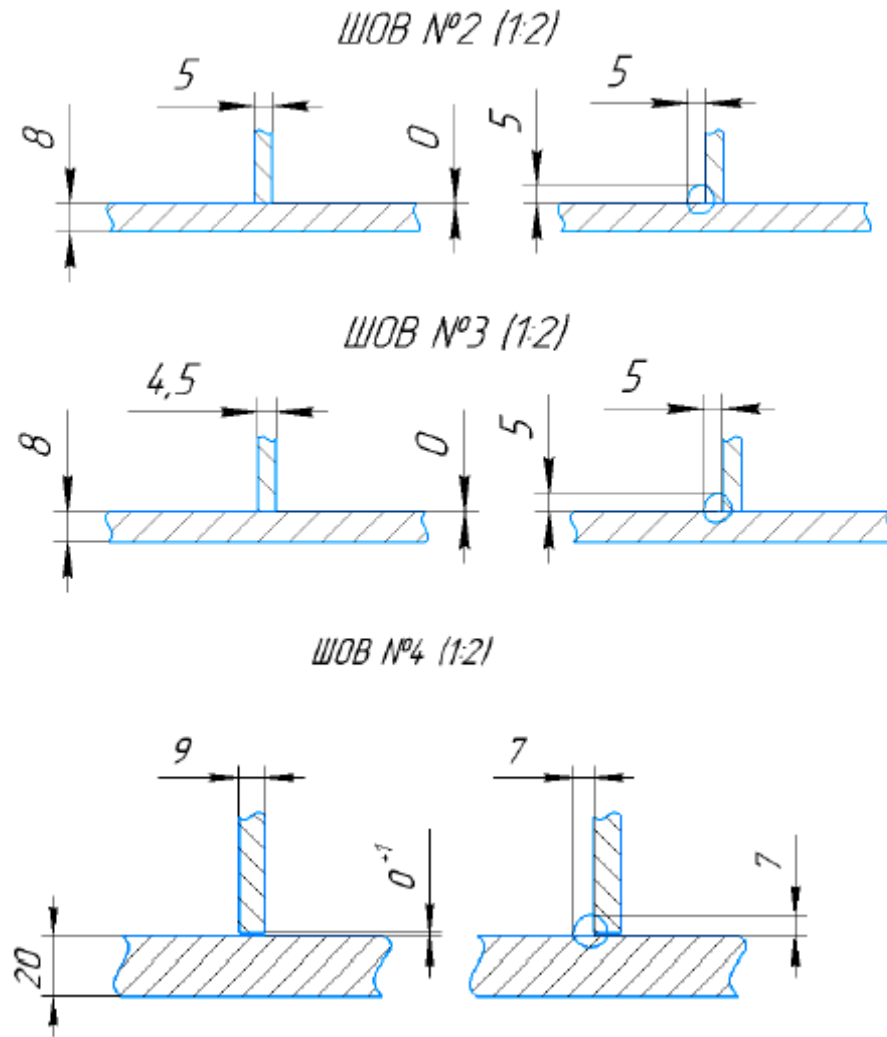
Геометричні розміри підготовки кромки для зварювальних швів №2,3,4
